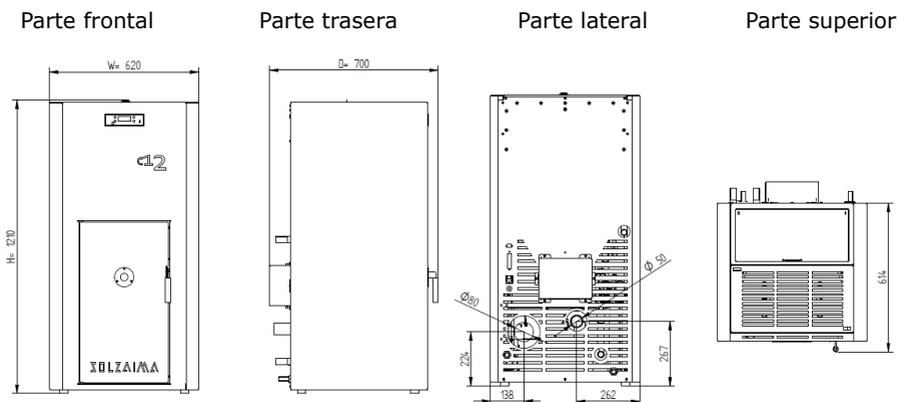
Dimensiones de la Compacta 12 kW de pellets
